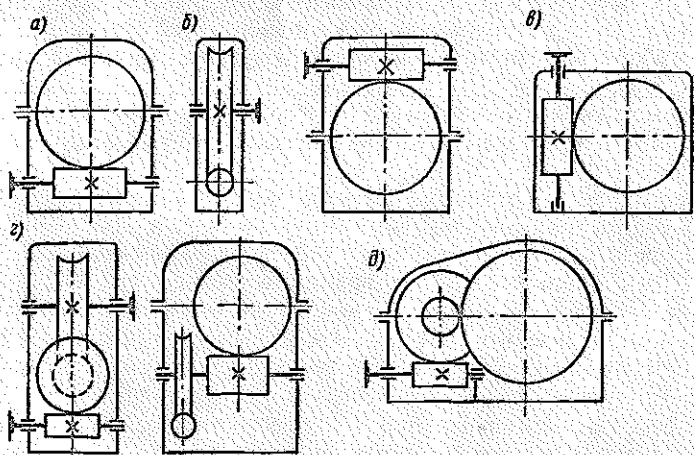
Схемы червячных и червячно-цилиндрических редукторов: а — б — одноступенчатые с горизонтальным нижним (а), верхним (б) и вертикальным расположением вала червяка; в — двухступенчатый; г — червячно-цилиндрический
